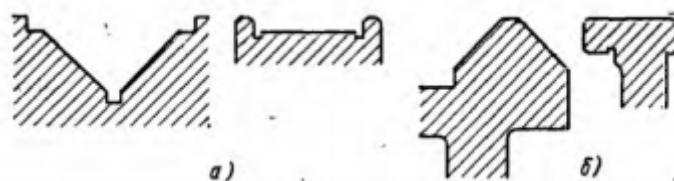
Направляющие охватывающие (а) и охватываемые (б).
